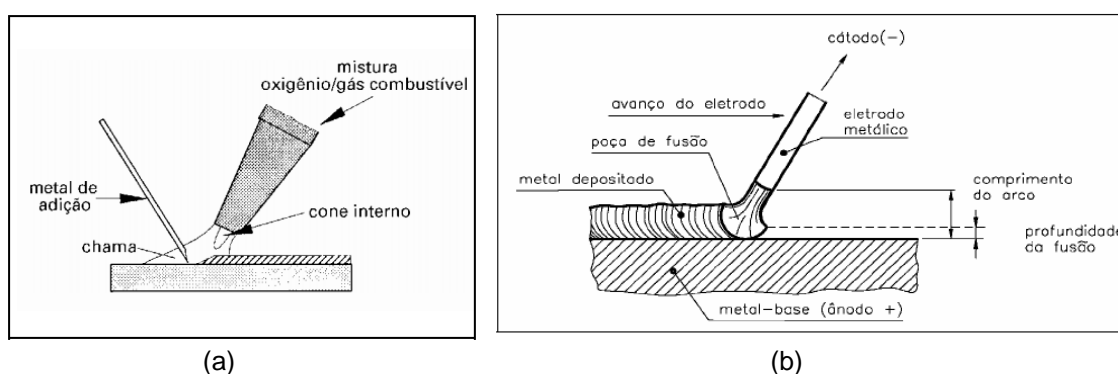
a) Soldagem à Gás; b) Soldagem a arco elétrico.
